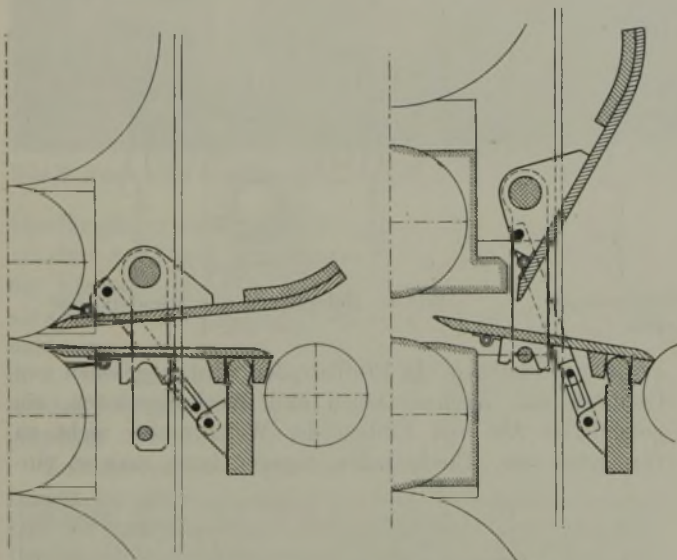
Walzarmatur zu einem Vierwalzengerüst.
